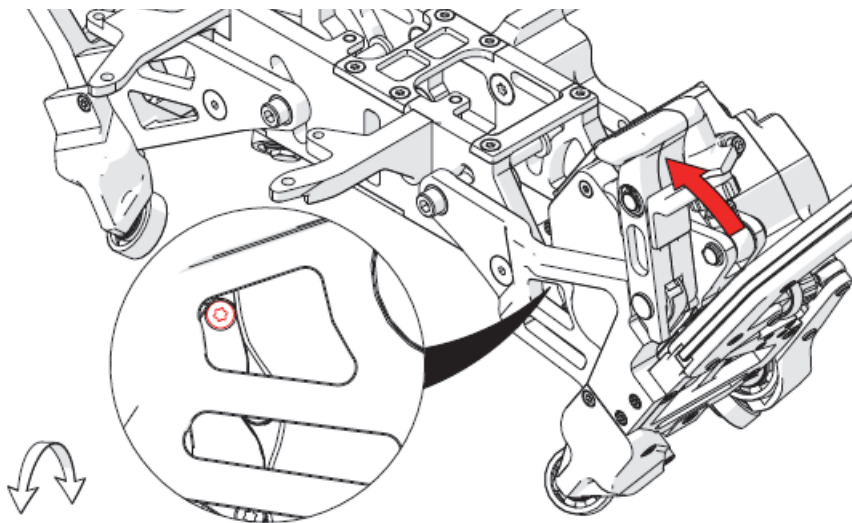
Extracción del tornillo Torx a partir de la parte superior del protector de la rueda de conducción
